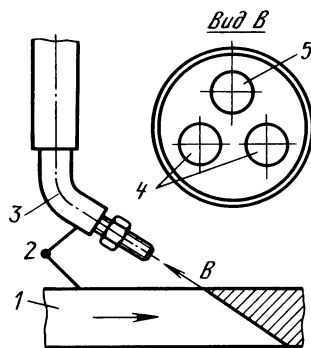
Схема резки «смыв-процессом»: 1 — разрезаемый металл, 2 — плавающее устройство, 3 — положение резака при резке, 4 — каналы для шлифующих (смывающих) струй кислорода, 5 — канал основной (режущей) струи кислорода
